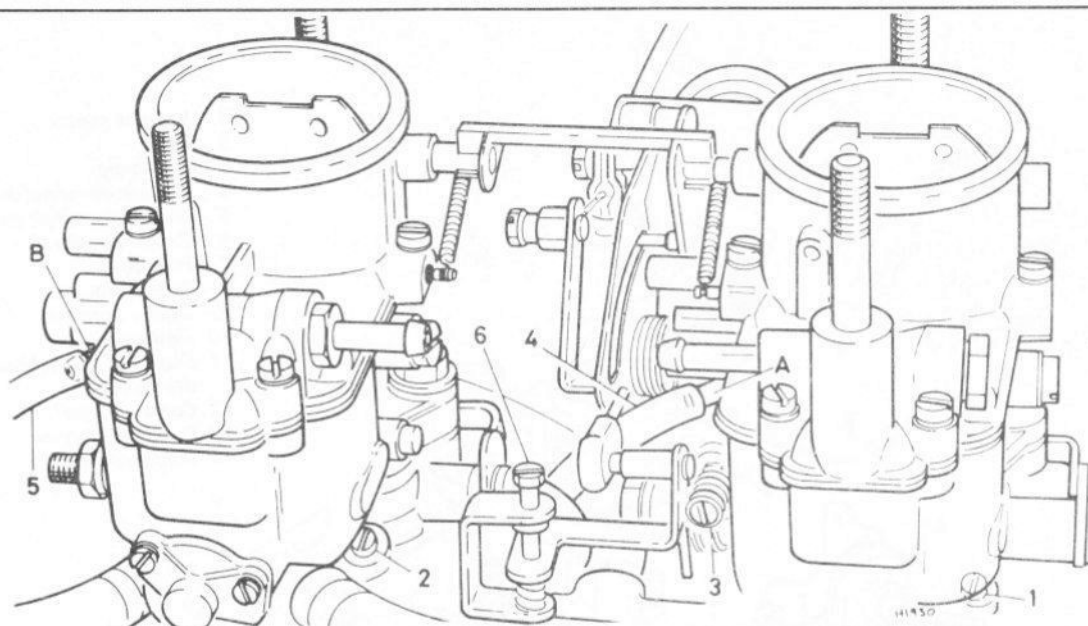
Positions des vis de réglage – carburateurs Weber 35 IBSH (Sec 8)
